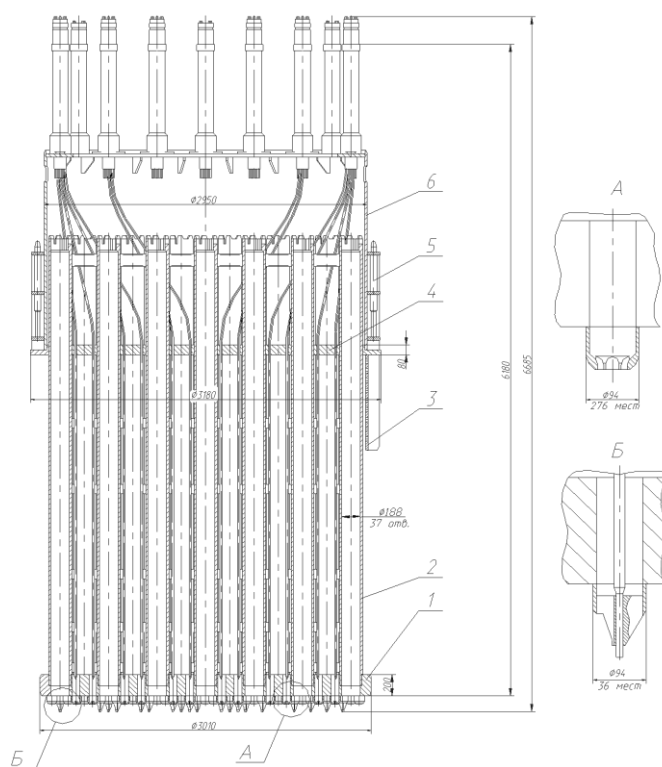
Общий вид блока защитных труб: 1 – нижняя плита; 2 – труба защитная; 3 – щит отбойный; 4 – верхняя плита; 5 – пружинный блок; 6 – обечайка
